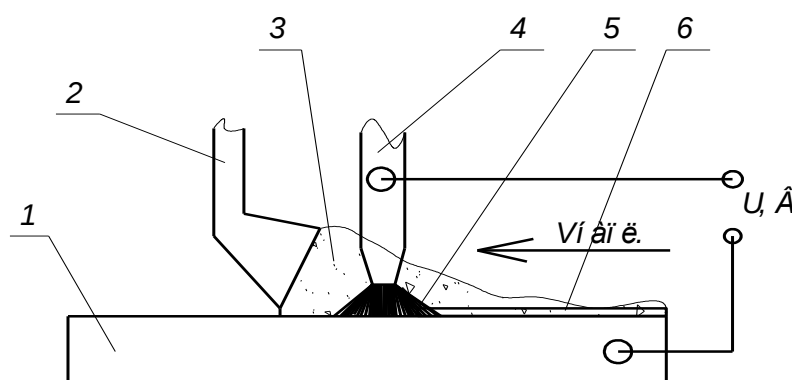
Схема автоматичного наплавлення під шаром флюсу
